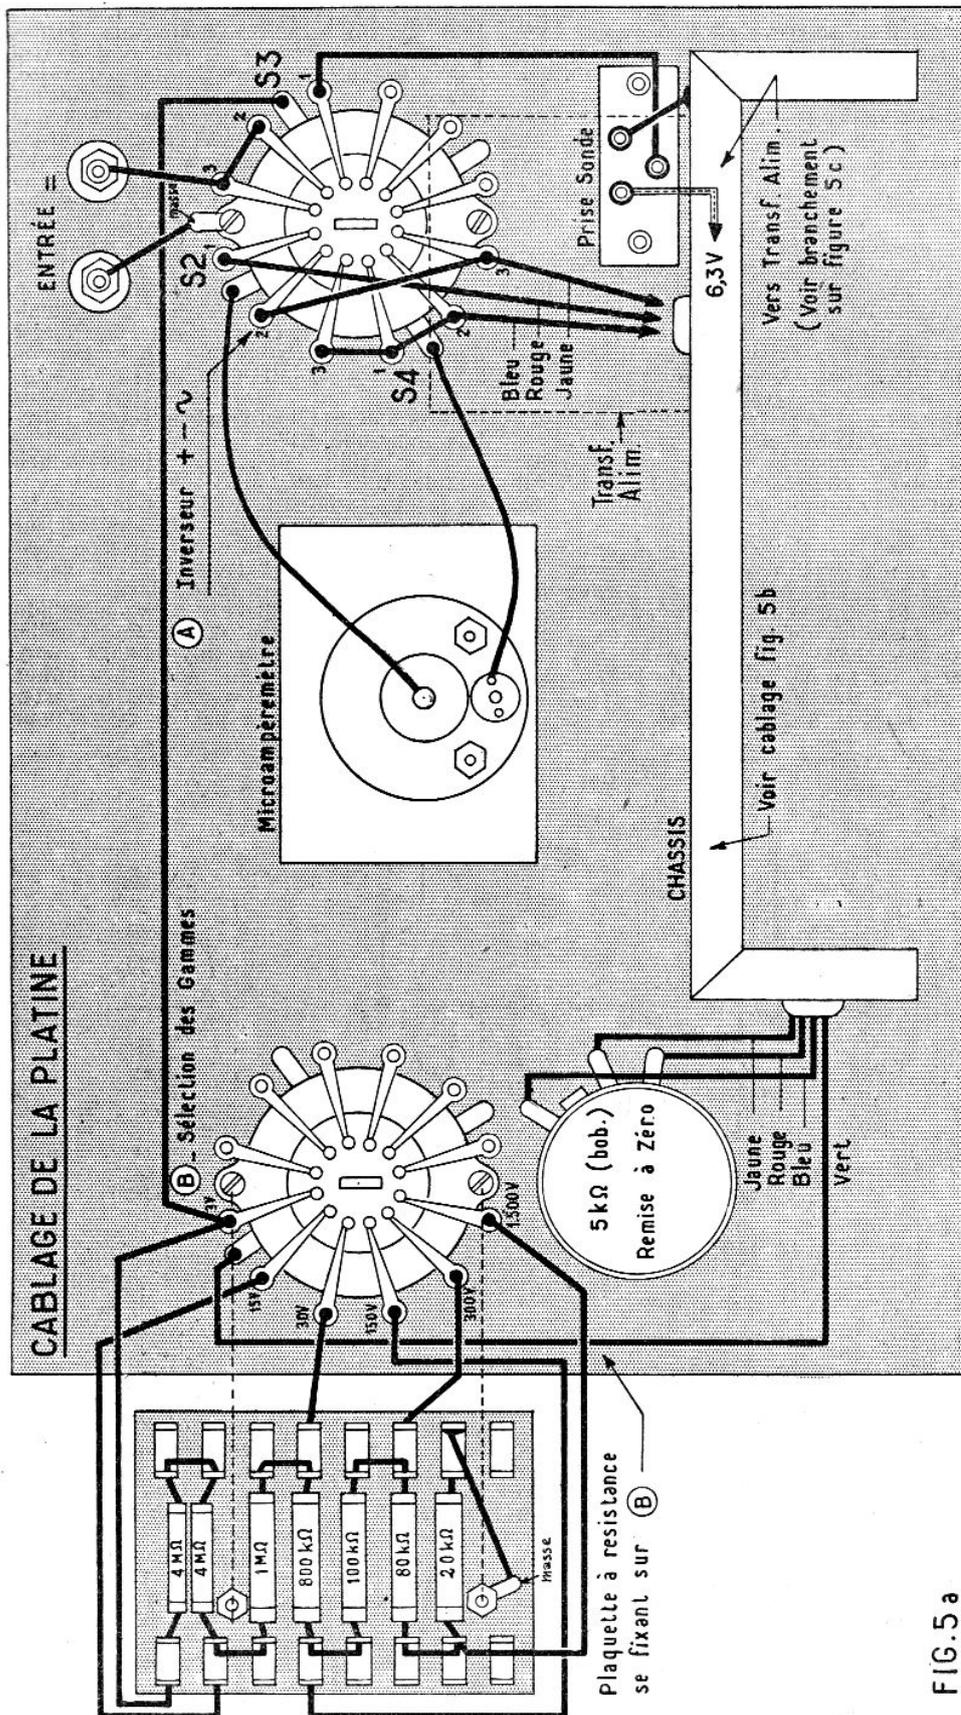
Plan de câblage de notre voltmètre et de la sonde.
